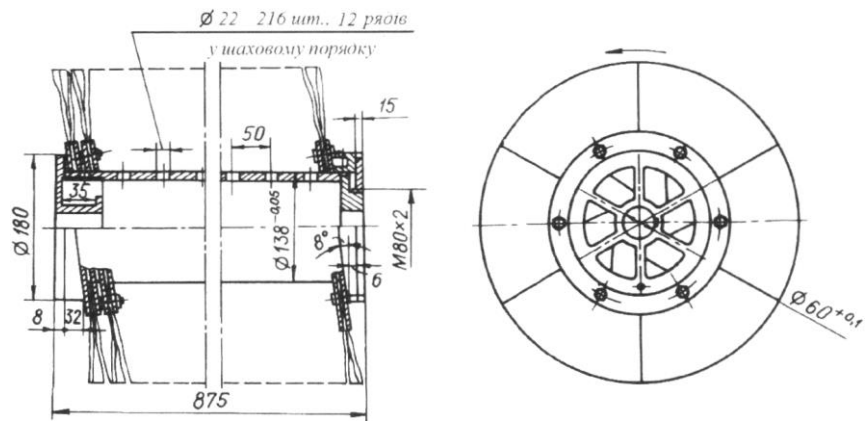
Пустотіла вентиляційна насадку (конструкції УкрНДІМОД)
